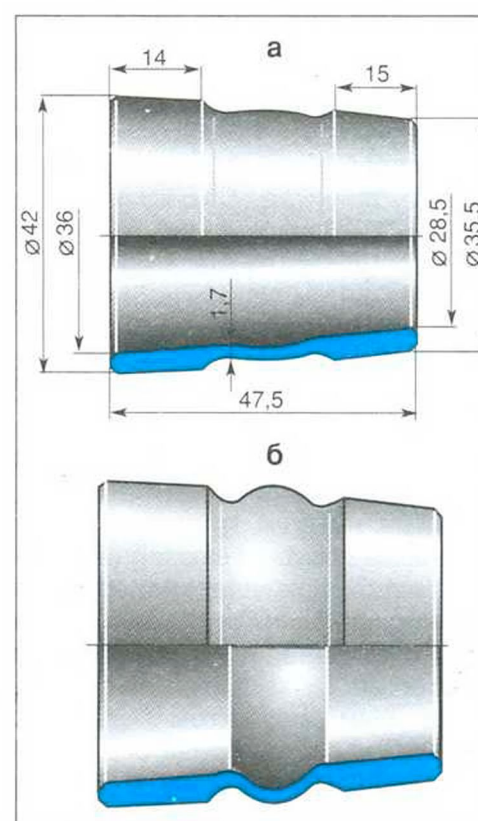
Распорная втулка подшипников: а - нормальная; б - деформированная
